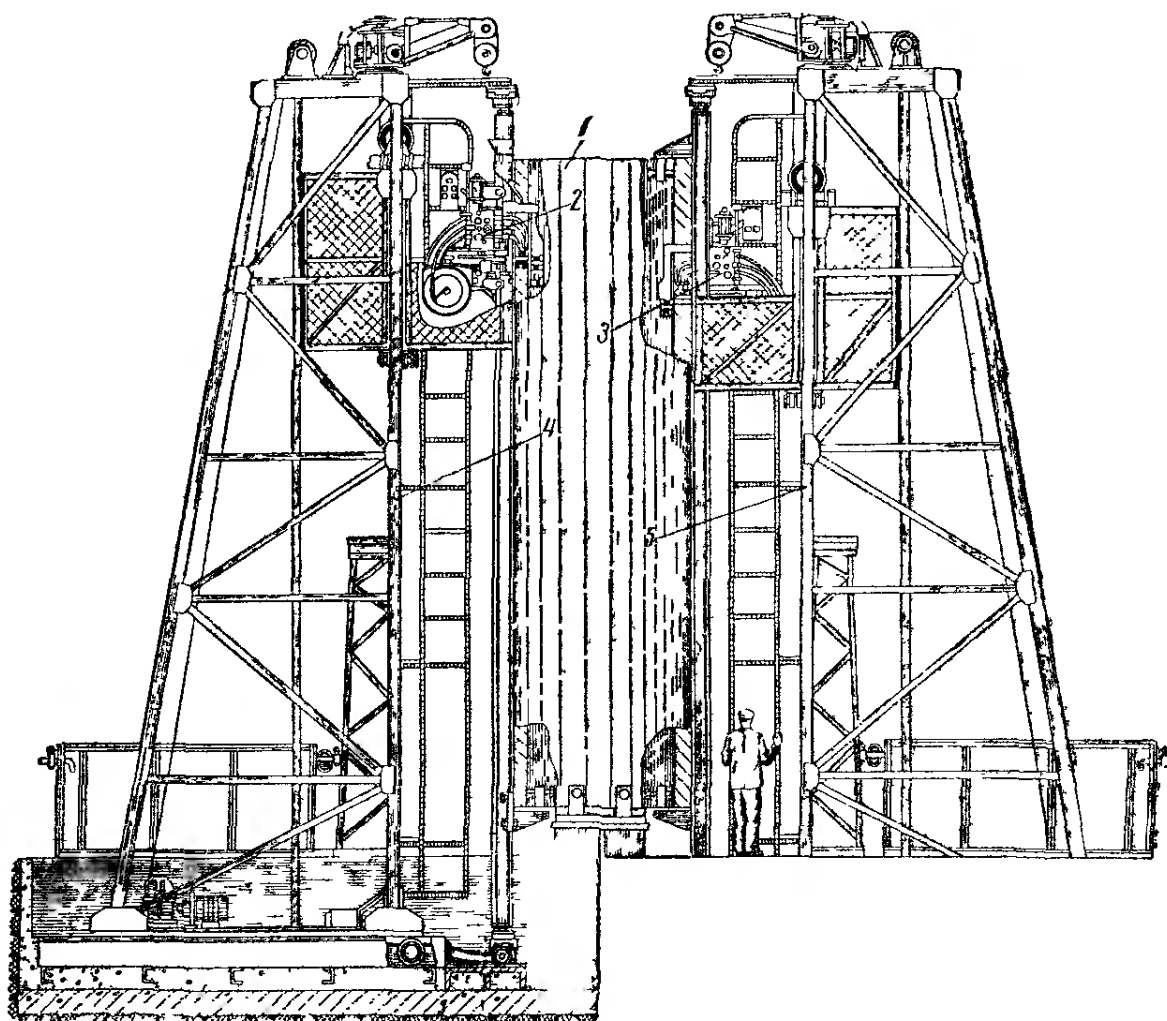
Установка для электрошлаковой сварки продольных швов
